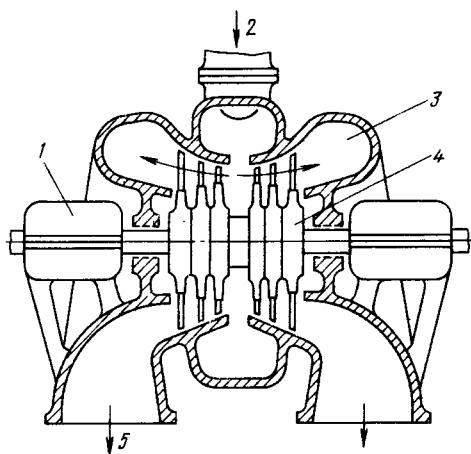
Конструктивная схема двухпоточного ЦНД:
